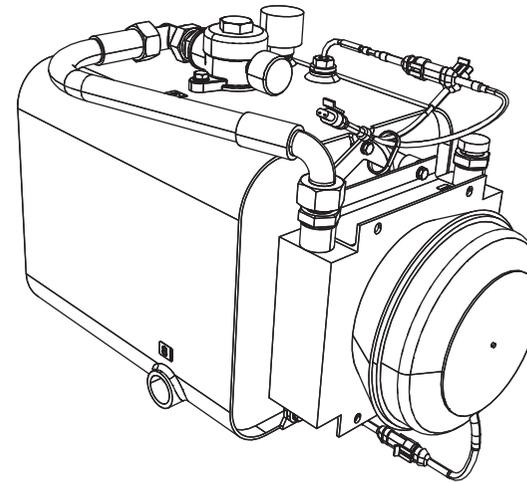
Öltank mit Kühler und Füllstandsmesser (400000 6831)
